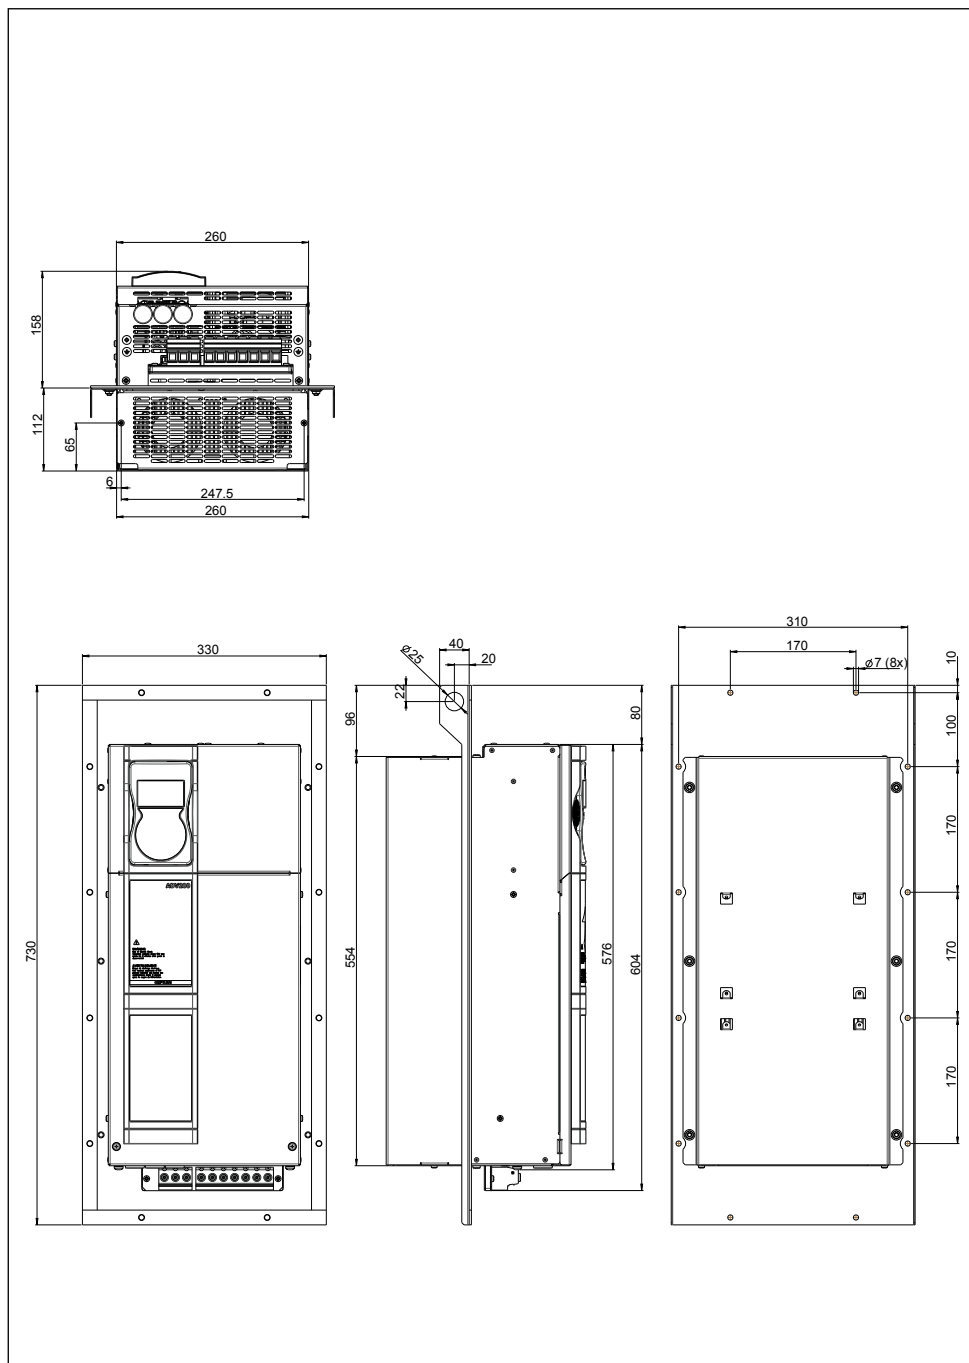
Размеры для типоразмера 5 (ADV200-...-EH)
